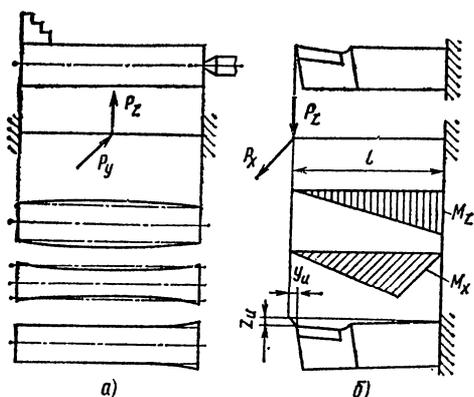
Схемы сил, действующих на заготовку (а) и резец (б)
